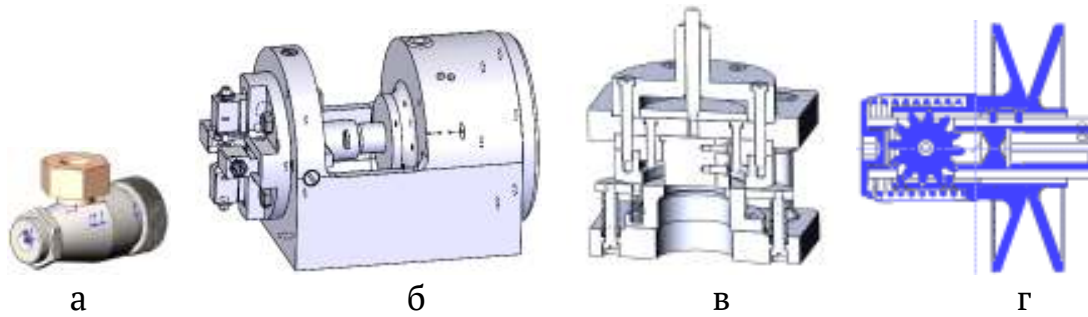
Форсунка (а), пристосування для хрестового обтиску прутка (б), штамп для виготовлення пластин (в), клинопасовий варіатор (г)
